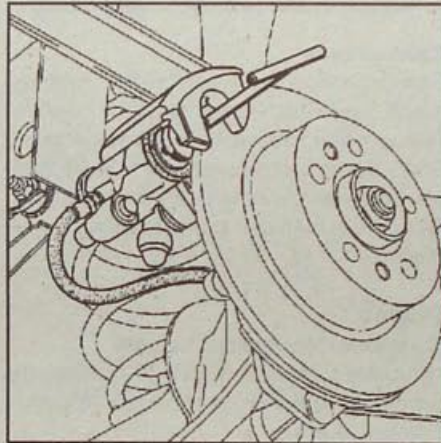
Использование приспособления Fre. 1190 для вворачивания поршня в суппорт
